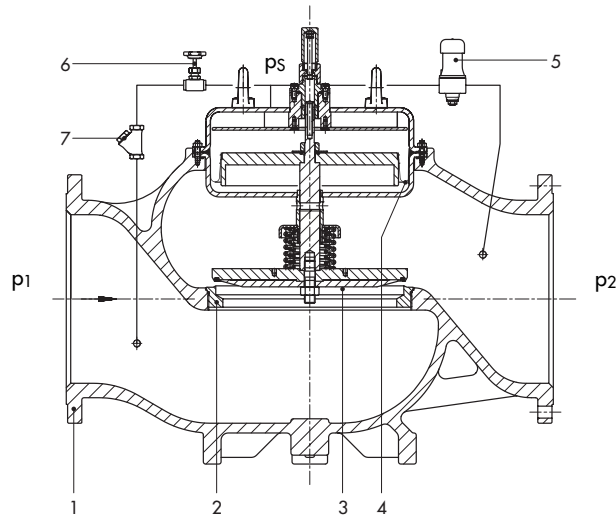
· Drukreducer type 2333 (DN 300 en DN 400), werking
